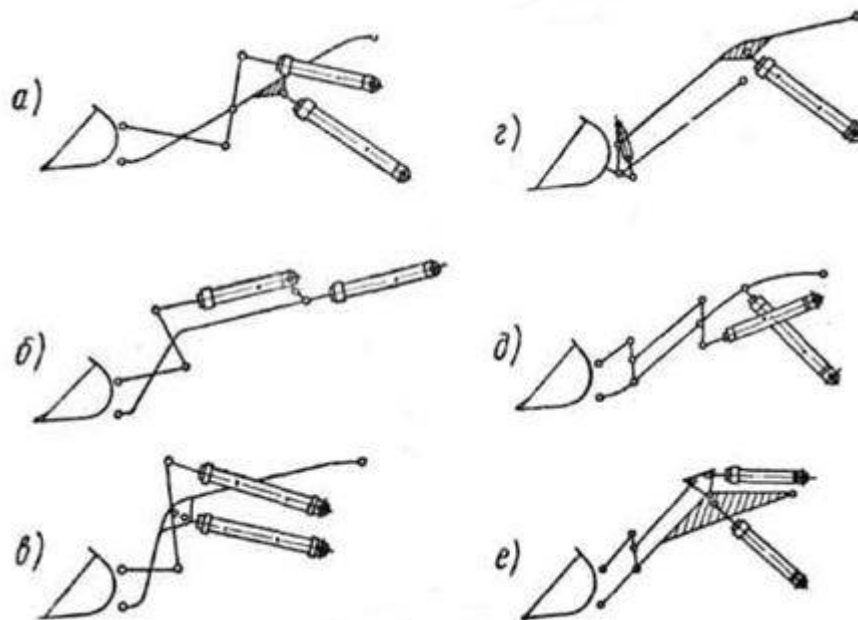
Конструктивні схеми навісного устаткування навантажувача: а-д – фронтальних; е – напівповоротних
